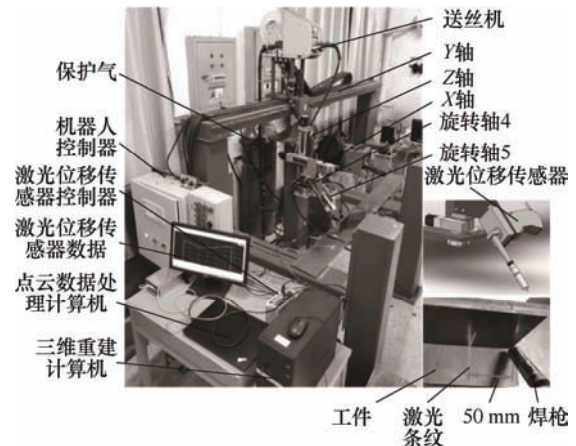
3D 折线焊缝跟踪机器人系统实物图
